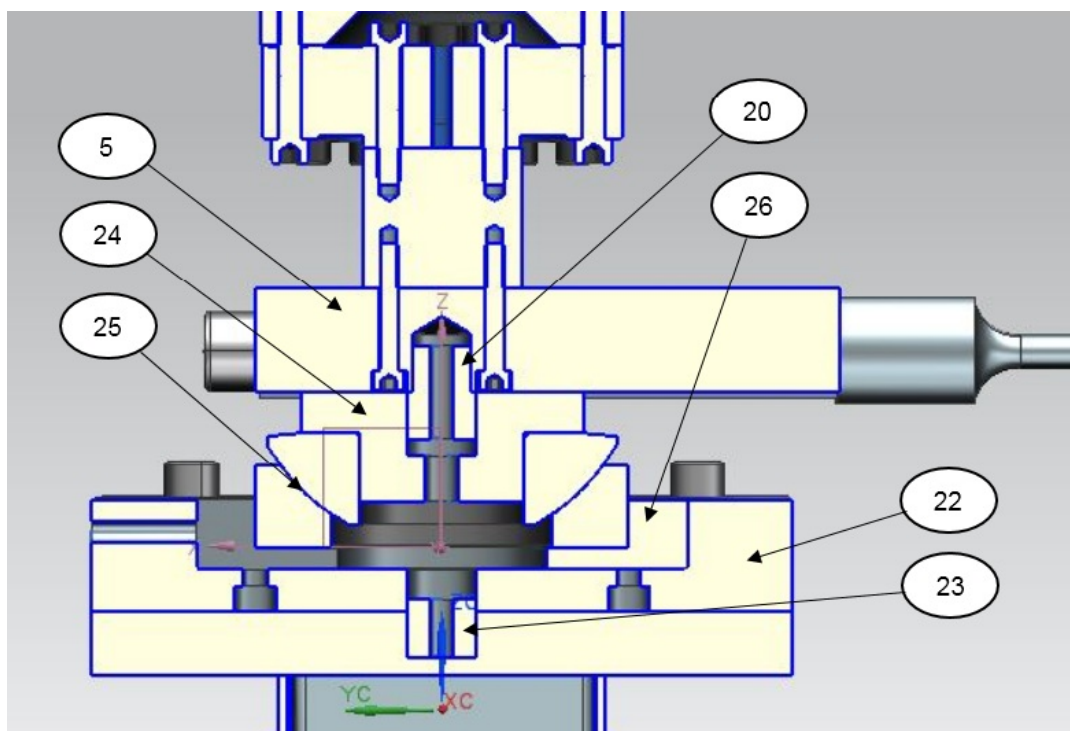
Schnitt durch das Modul GE 70 AW bestehend aus: Horizontalblock (5), Befestigungsbolzen (20), Adapter GE 70 AW Kugel (24), GE 70 AW (25), Adapter GE 70 AW Pfanne (26), Modulgrundplatte (22), Zentrierbolzen (23).
